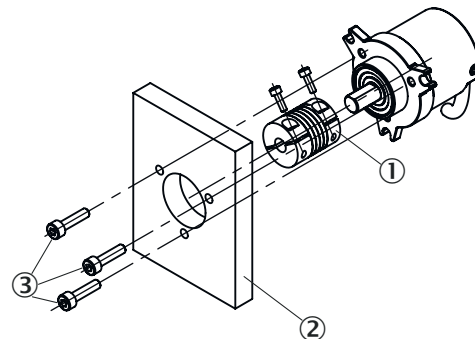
Anbau Klemmflansch 3xM3 über flanschseitige Gewindebohrungen
